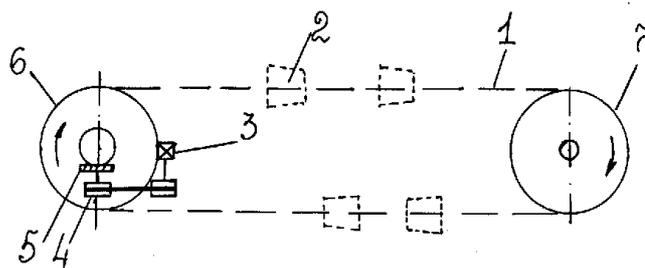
Схема передачи движения цепному конвейеру
